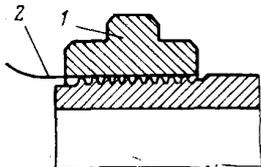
Схема проверки конусности наружной резьбы ТТ гладким калибром и щупом:
